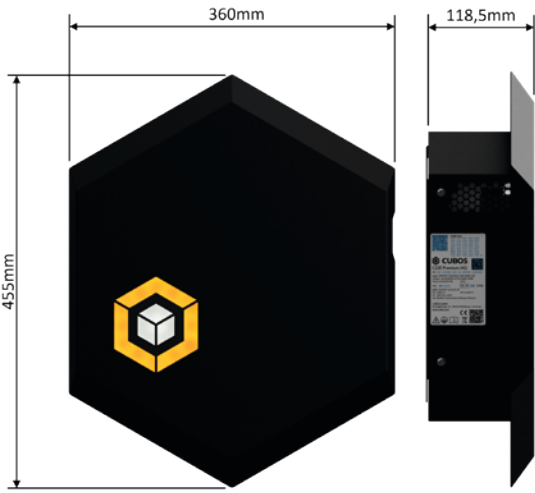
Frontalansicht Wallbox geschlossenes Gehäuse (links); Seitenansicht Wallbox (rechts); ohne Ladestecker
